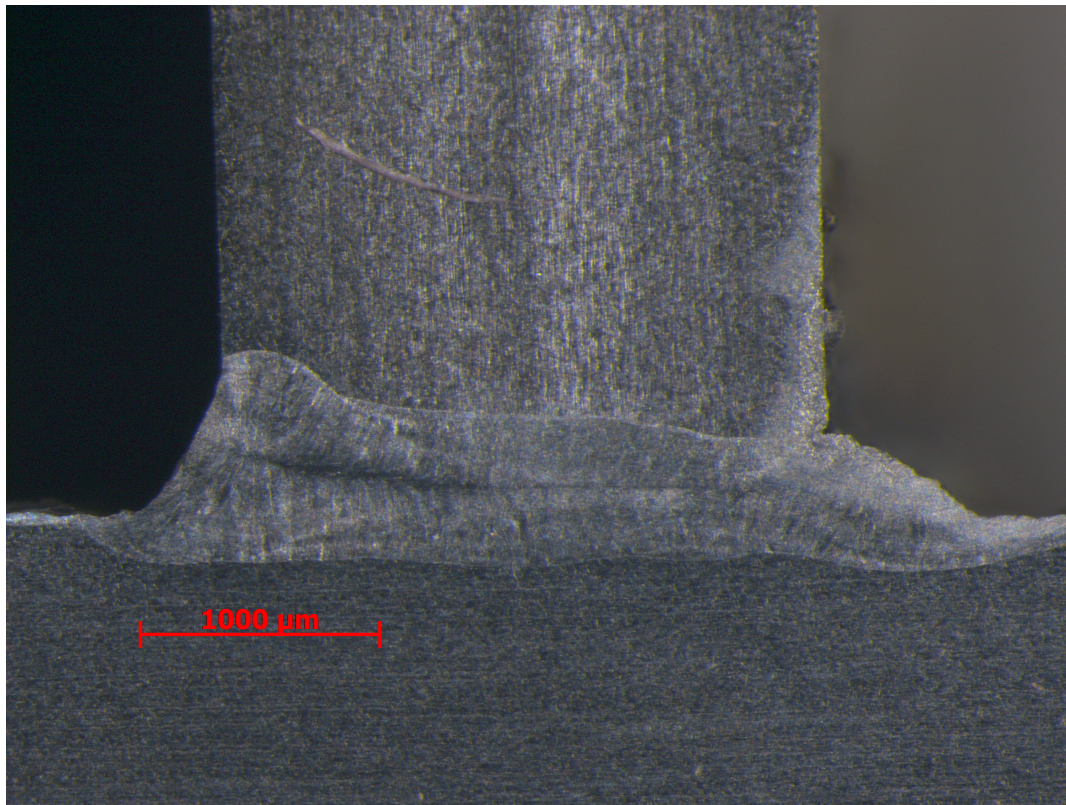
Vue en coupe du cordon de soudure débouchant.
